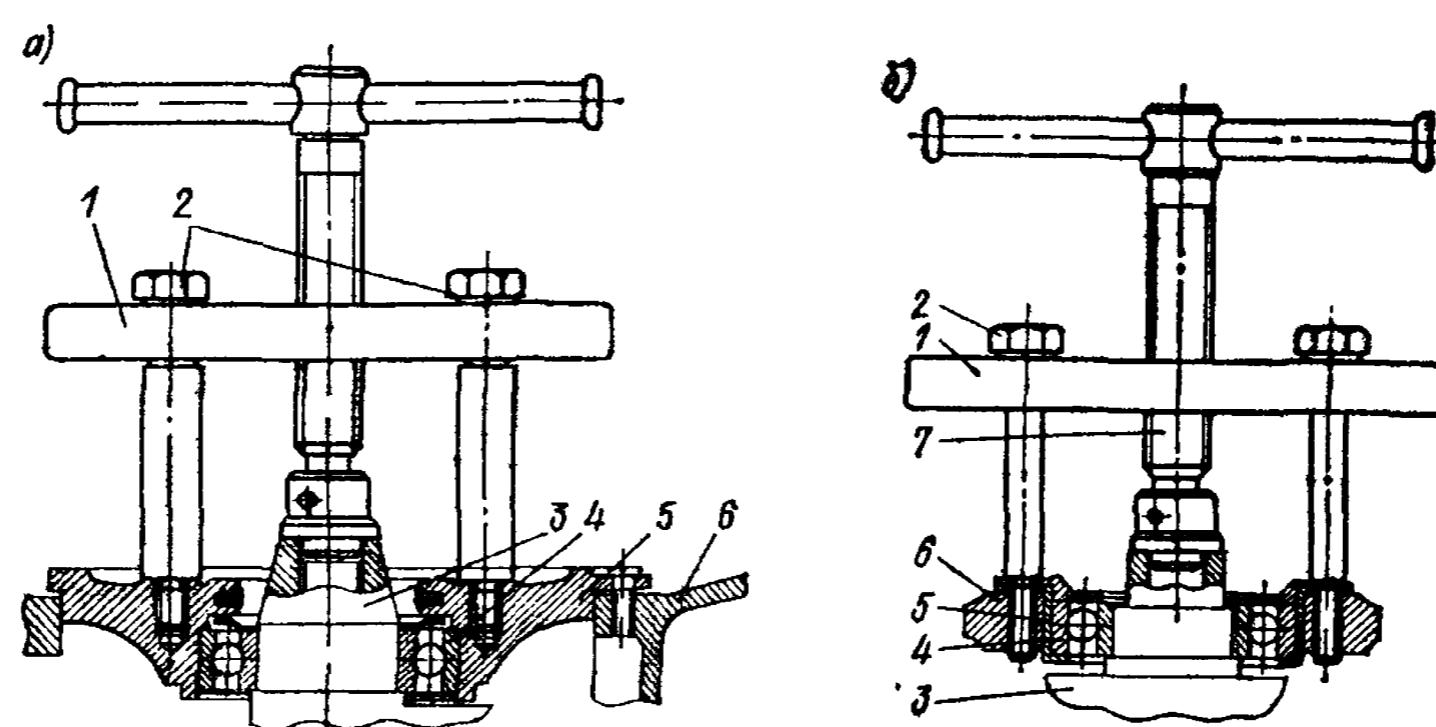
Выпрессовка коленчатого вала с помощью универсального съемника:
